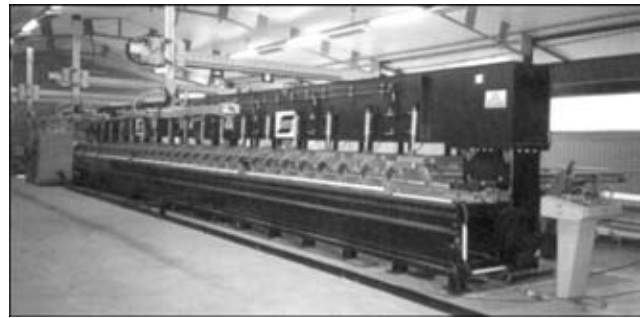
Установка ESAB Super Stir™ для сварки прессованных панелей, поставленная на фирму «Marine Aluminium» (Норвегия)
